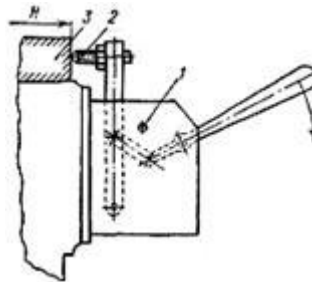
Важільно-шарнірний механізм як швидкодіючий ручний затискач
